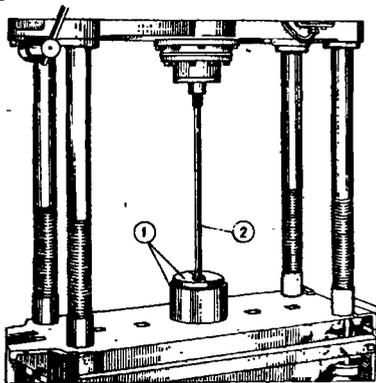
Выпрессовка запорного кольца подшипника полуоси приспособлением А.74108/Р: 1 - приспособление А.74108/Р; 2 - полуось
